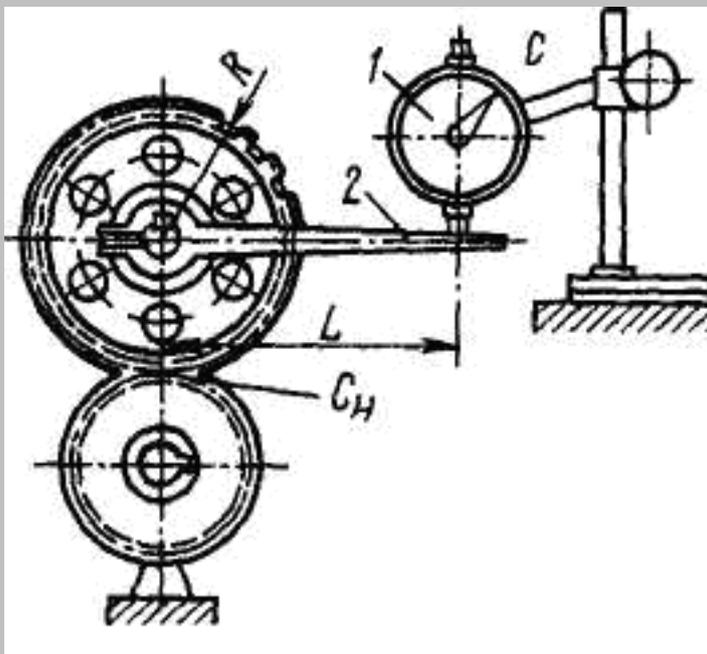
Измерение бокового зазора в цилиндрической зубчатой передаче: 1 — индикатор, 2 — поводок
